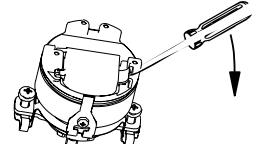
Imagen del montaje de SKS36S/SKM36S árbol cónico
